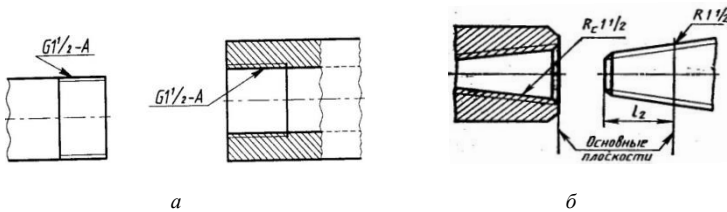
Простановка размеров трубной резьбы: *а* – цилиндрической; *б* – конической
